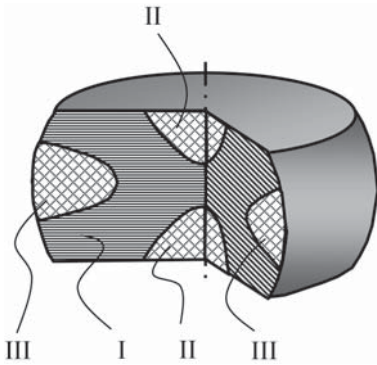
Зоны деформации в осаживаемой цилиндрической заготовке
